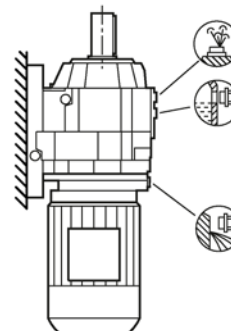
Монтажные положения для цилиндрического редуктора D/Z в исполнении на лапах, типоразмеры 19–29
